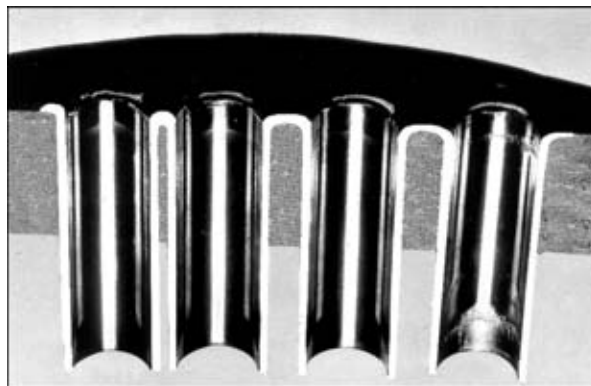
Макрошлиф сварных соединений трубной решетки (BT1-0) с трубками (Э125)
